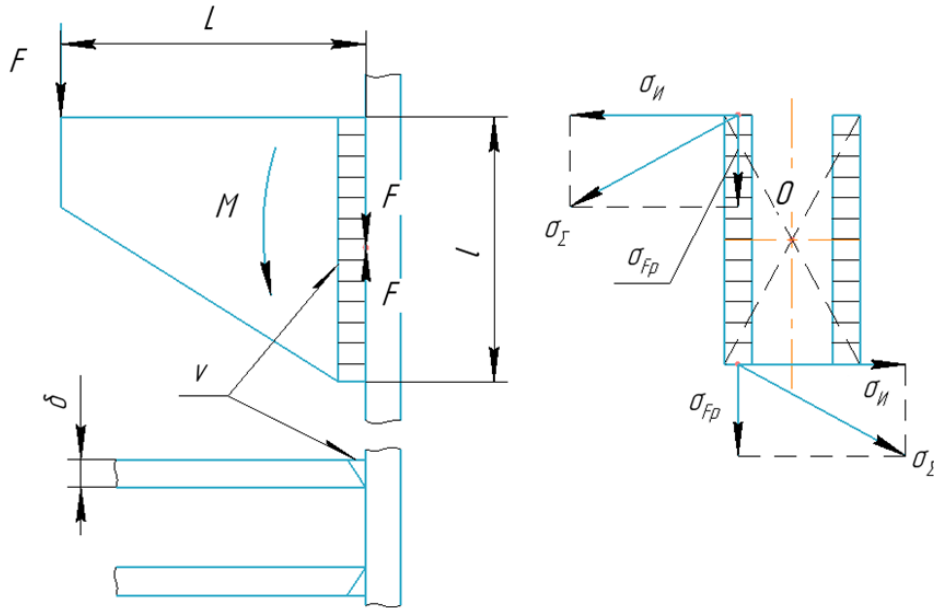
Расчетная схема сварного соединения стыковым швом
